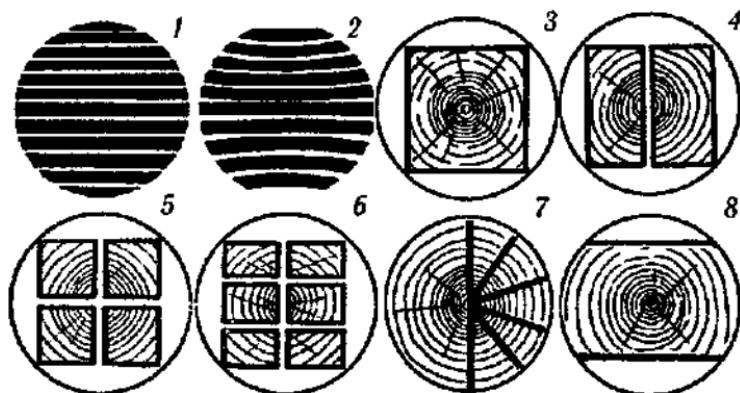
Виды пиломатериалов: 1 — распиловка дерева на доски; 2 — доски после усушки; 3 — брус; 4 — обрезные пластины; 5 — обрезные четвертины; 6 — распиловка ствола на бруски; 7 — слева — пластина, справа — полено, расколотое на дрова; 8 — лежак.
